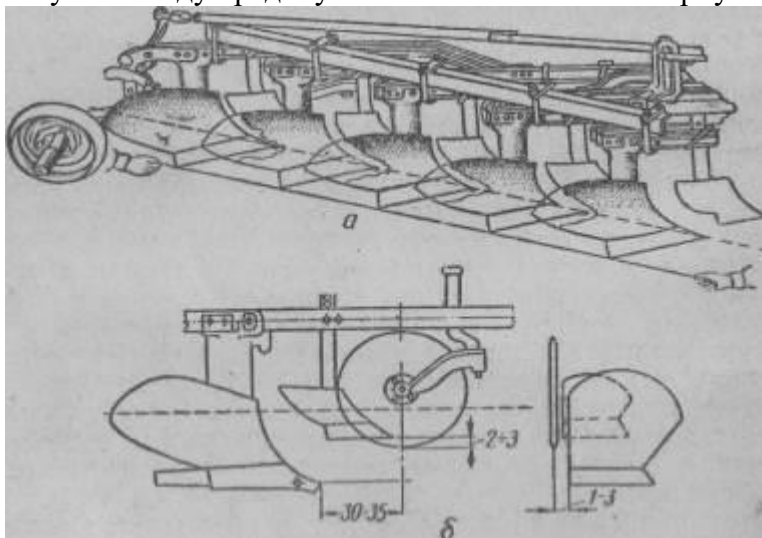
Установка плуга: а --проверка расположения корпусов; б -- установка продрялужимка- и ножа на раме плуга.
